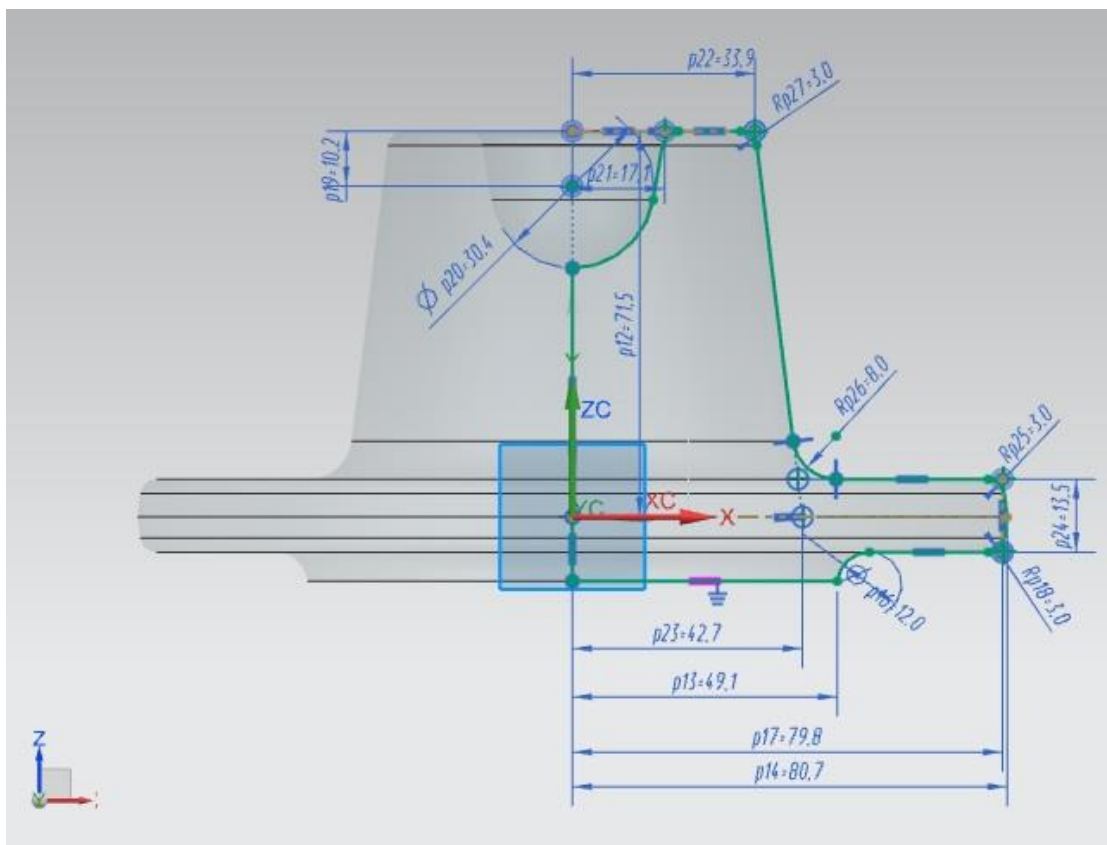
Ескіз гарячої заготовки деталі «Кришка»
